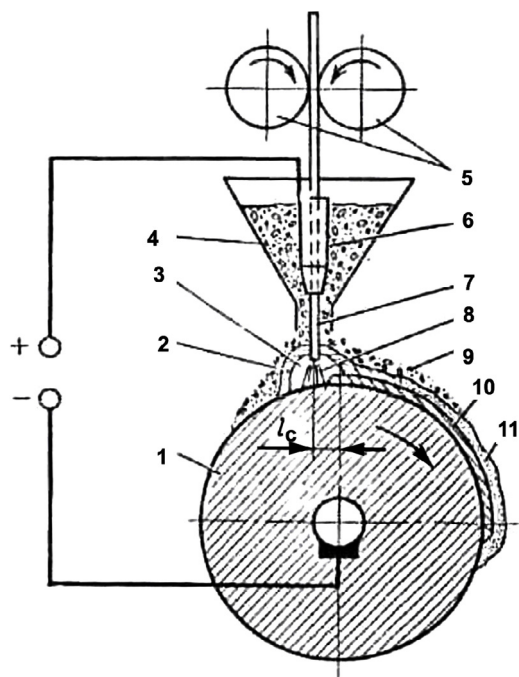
Схема автоматической наплавки вала под слоем флюса:
